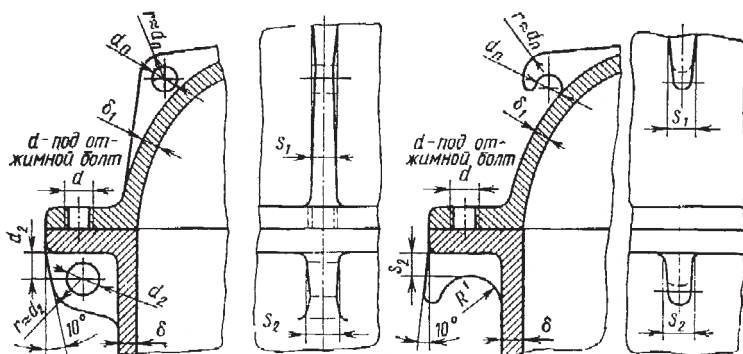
Крюки и проушины для транспортировки редуктора и его деталей
